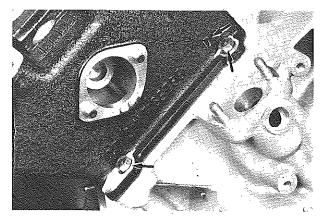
Marcatura teste e dadi anteriori Head marking and front nuts
